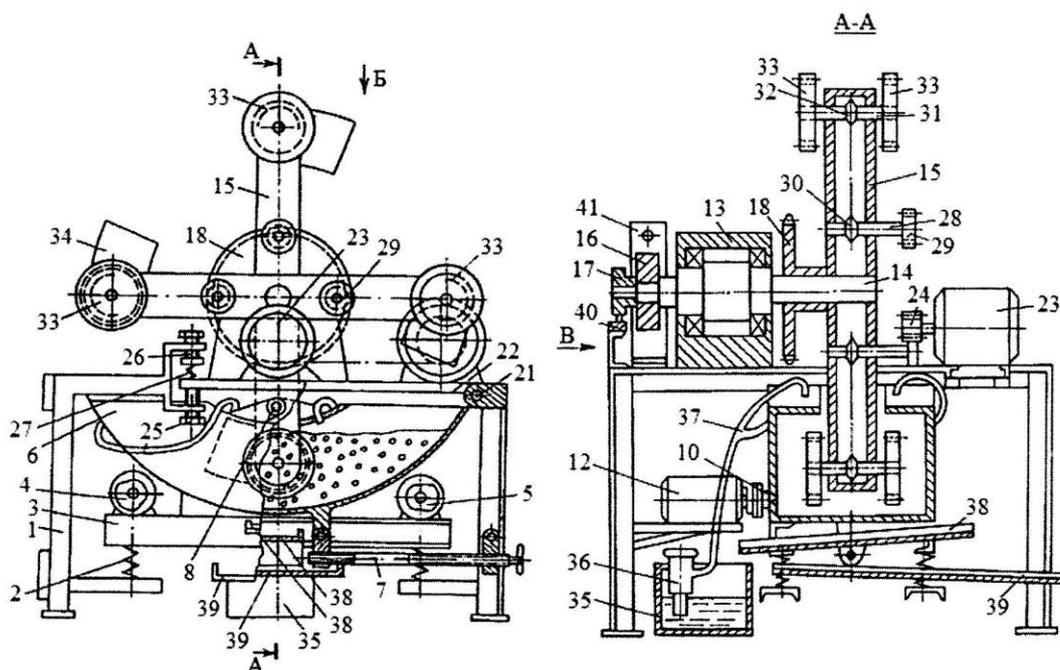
Станок для вибрационной обработки шестерен с совмещением сложного движения обрабатываемых предметов с колебательным движением рабочих тел:
